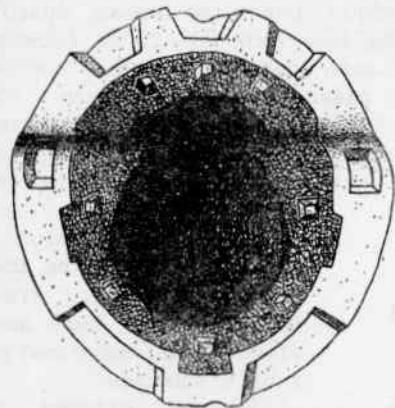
Клеевая форма и отливка черепа. Раскрыта форма. Верхняя часть.
